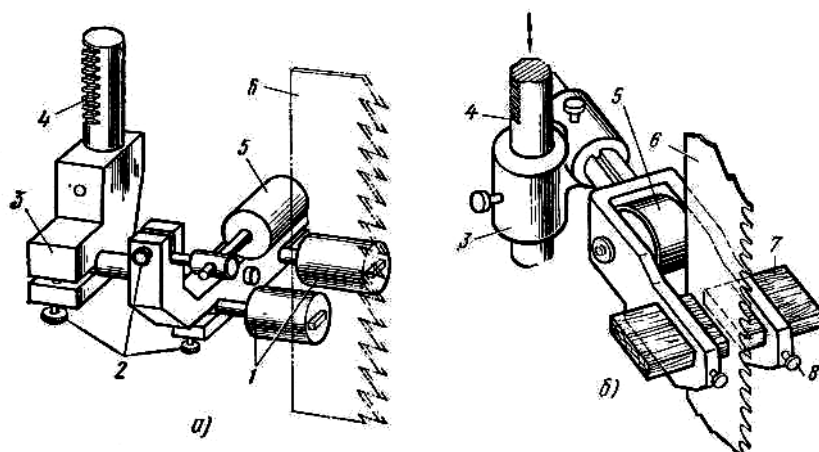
Направляющее устройство ленточнопильного станка: а — ролик, б — скольжения; 1 — ролики боковые, 2 — фиксатор, 3 — державка, 4 — штанга, 5 — ролик упорный, 6 — пила, 7 — бобышка, 8 — винт крепления
